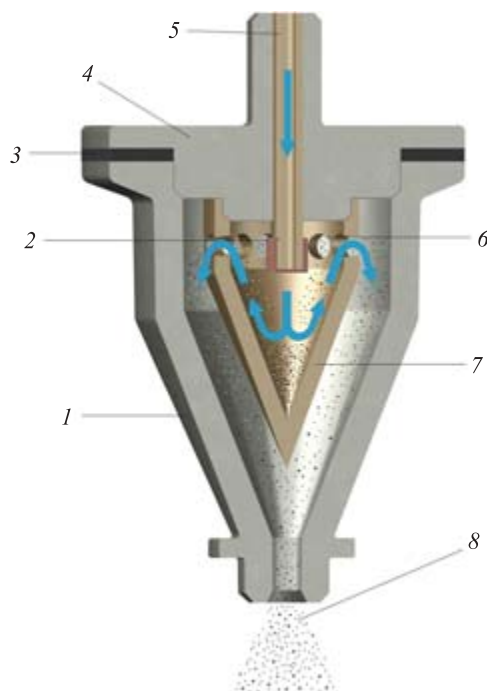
Конструкция устройства для подачи порошка: 1 — корпус; 2 — насадок; 3 — прокладка; 4 — основание; 5 — трубка; 6 — выходное отверстие для порошка; 7 — резервуар; 8 — газопорошковая смесь; ➔ — движение сжатого воздуха
